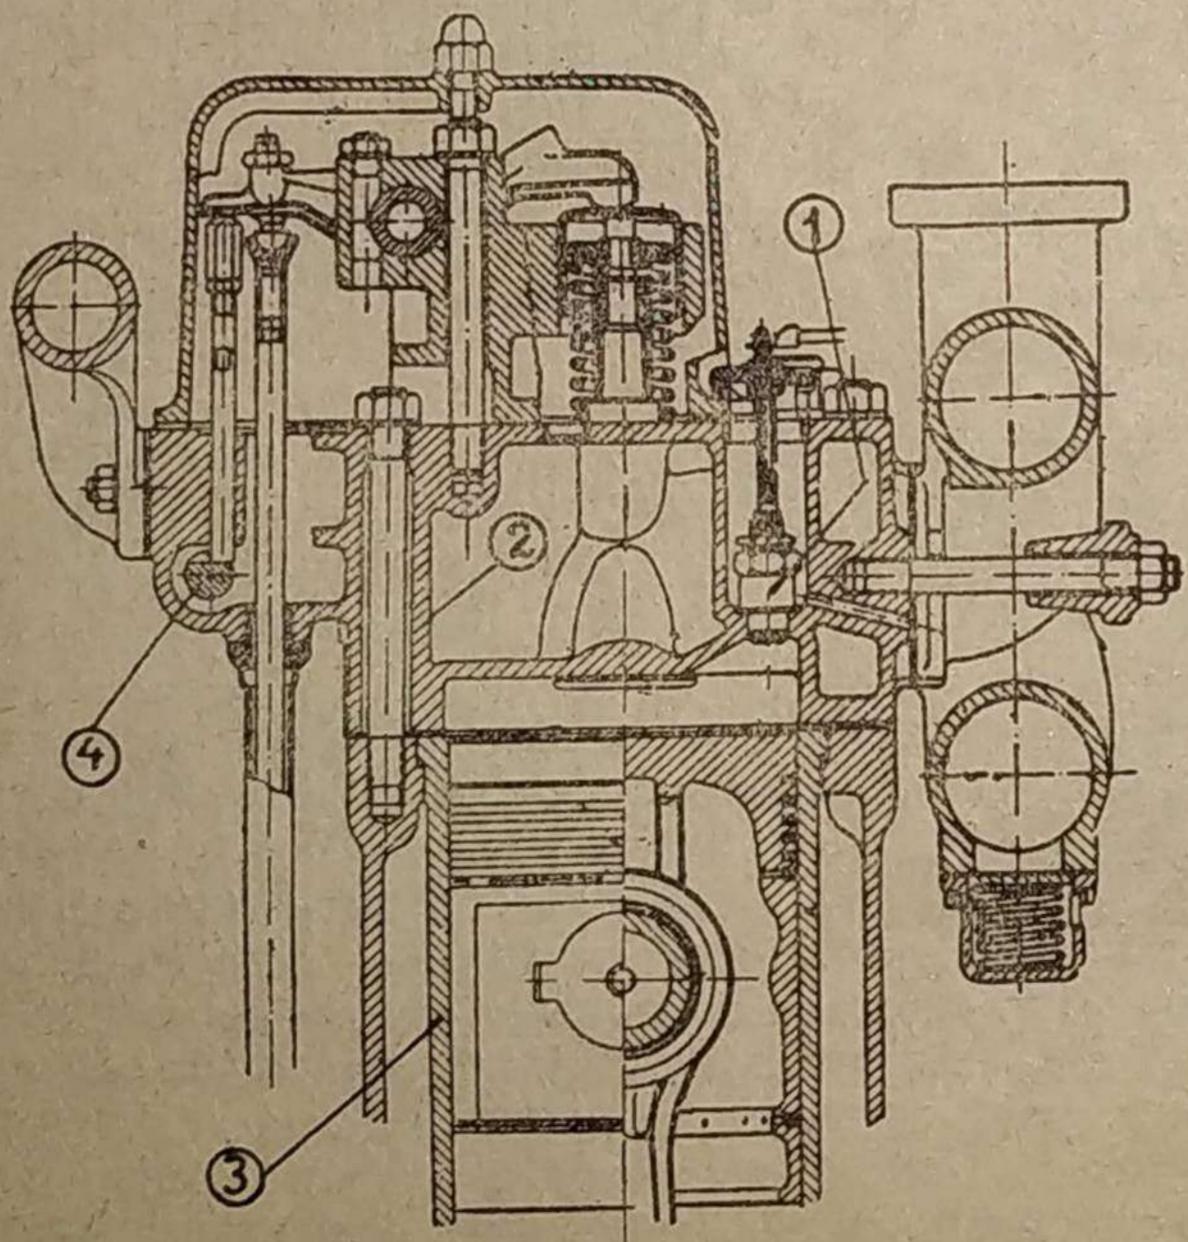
Головка и часть цилиндра двигателя «МГ-17».
